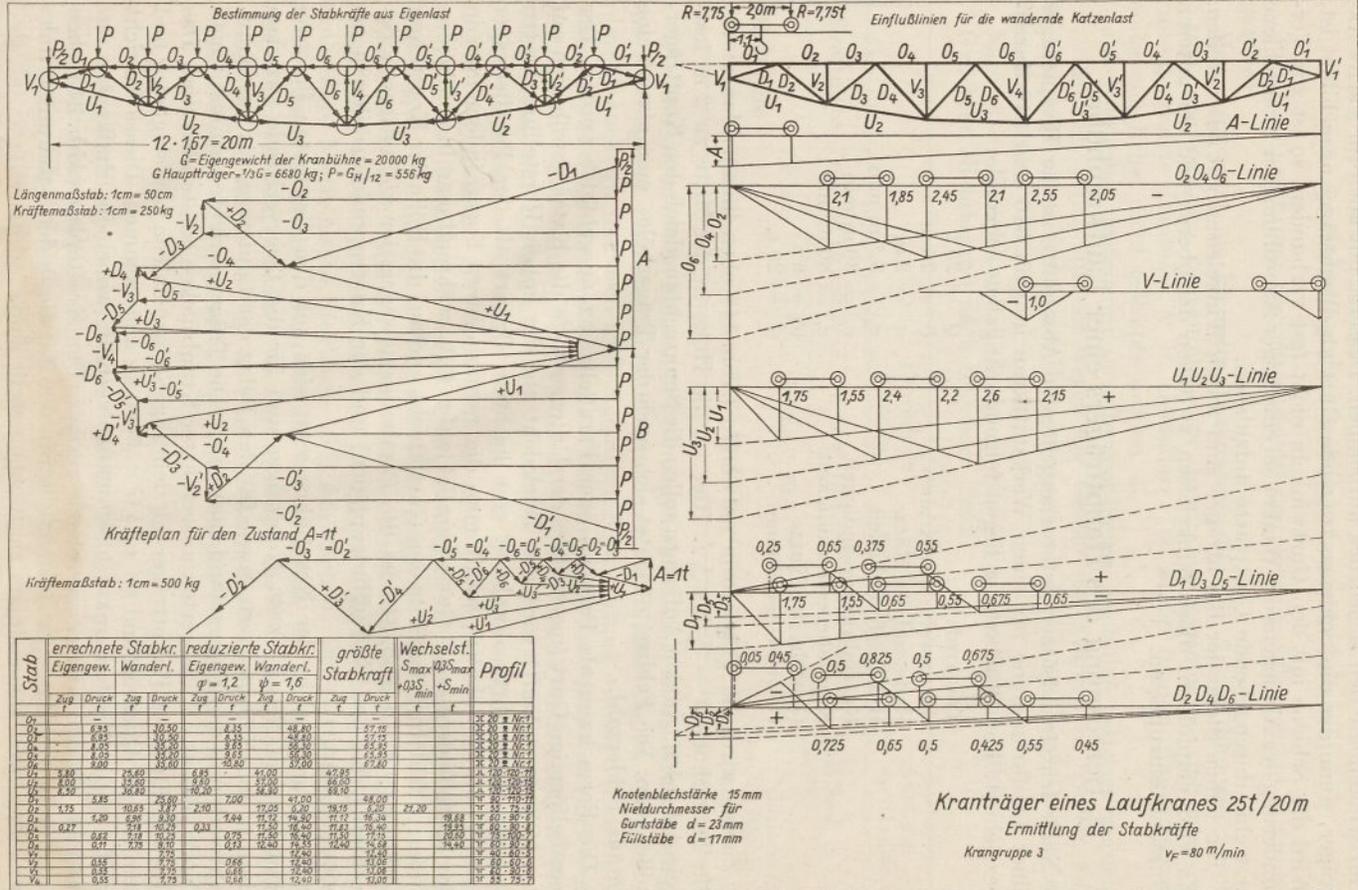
Statische Berechnung eines Laufkranhauptträgers (verkl. 1:5).
